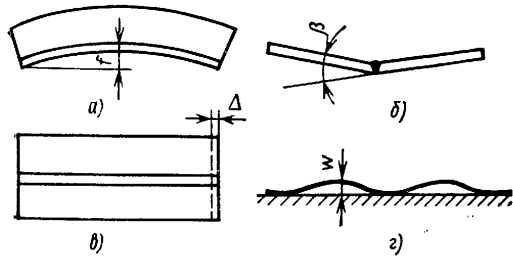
Виды перемещений в элементах сварных конструкций
